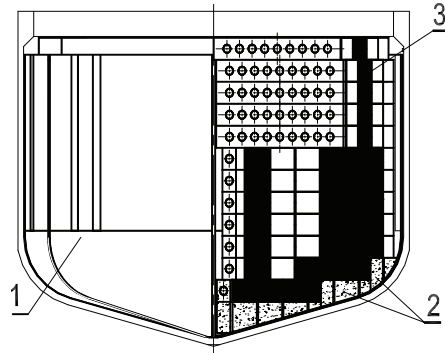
Схема размещения блоков наполнителя с ЖМ внутри корпуса УЛР: 1 – наполнитель с ЖМ; 2 – конический блок наполнителя; 3 – цилиндрический блок наполнителя
